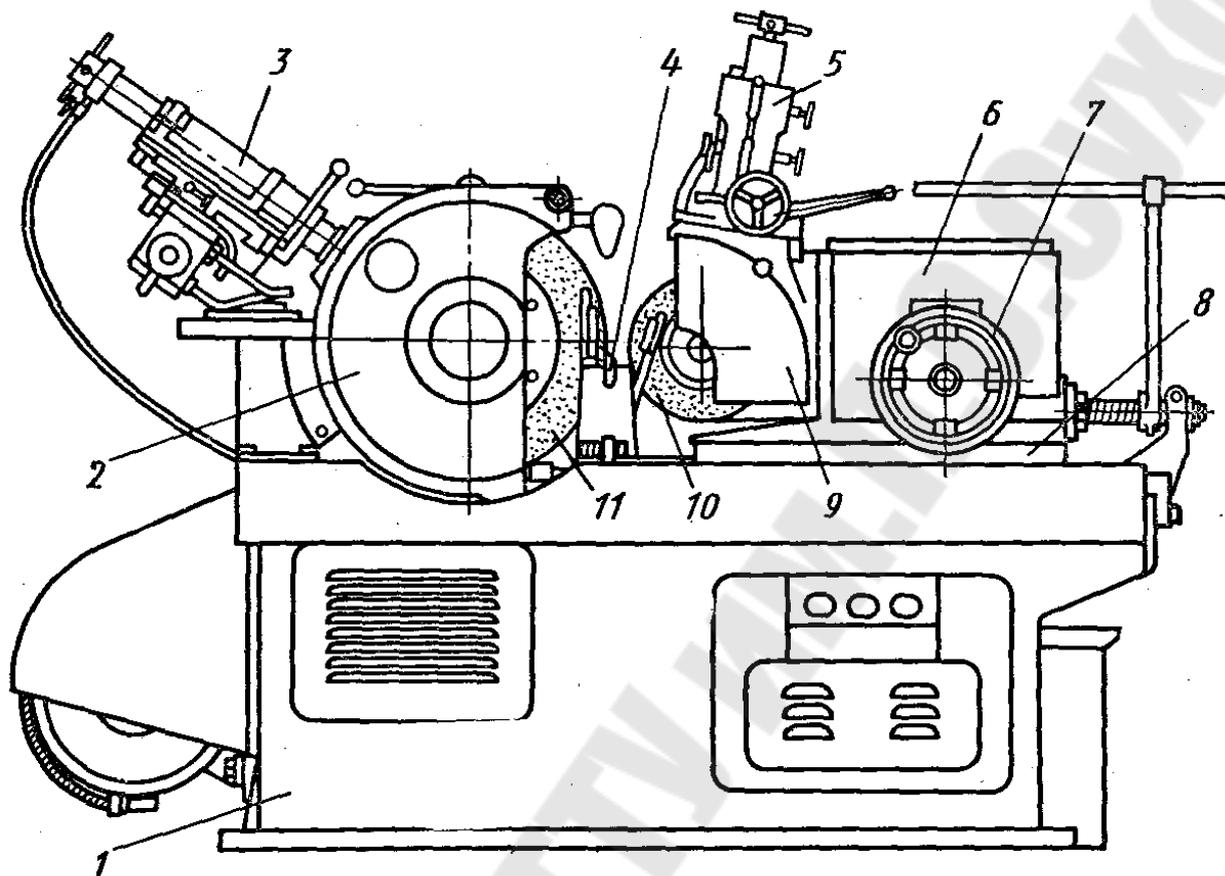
Общий вид бесцентрового кругло-шлифовального станка
